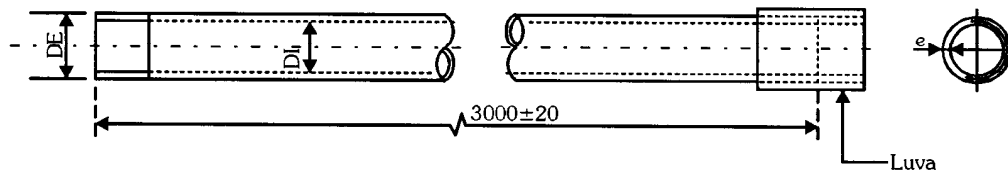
Corte Longitudinal e Corte Transversal de um Eletroduto
